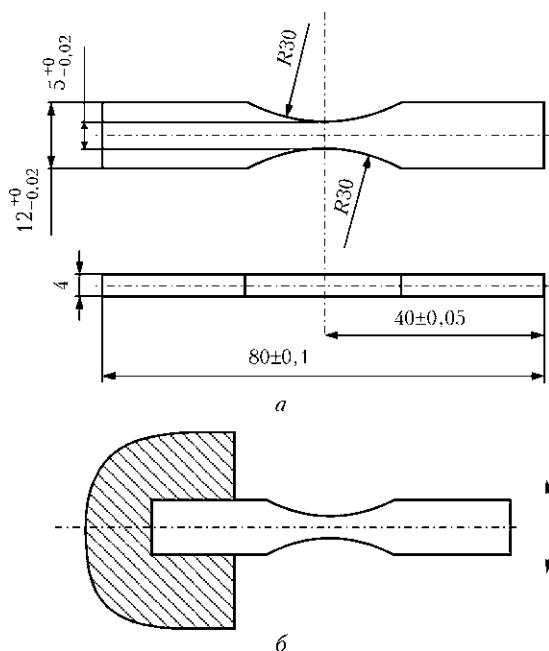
Эскиз образца для испытаний на усталость (а) и схема его нагружения (б)
